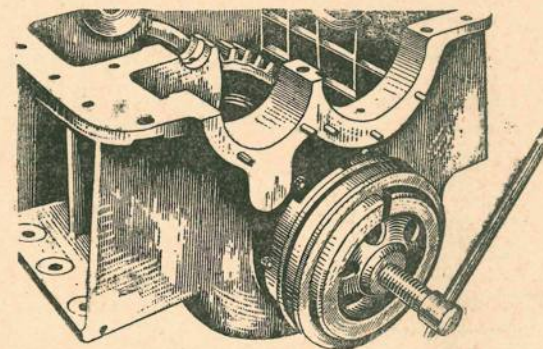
Снятие шестерни муфты полужесткого сцепления главного вала коробки перемены передач
